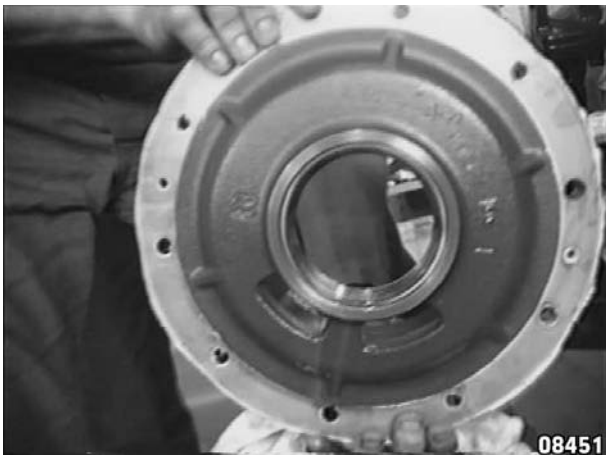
Monter le flasque de support du boîtier du différentiel en mettant en place le piston du frein et le disque du frein.
